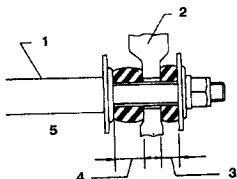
Положение установки втулки крепления толкающей штанги к цапфе (См. Раздел 10)
